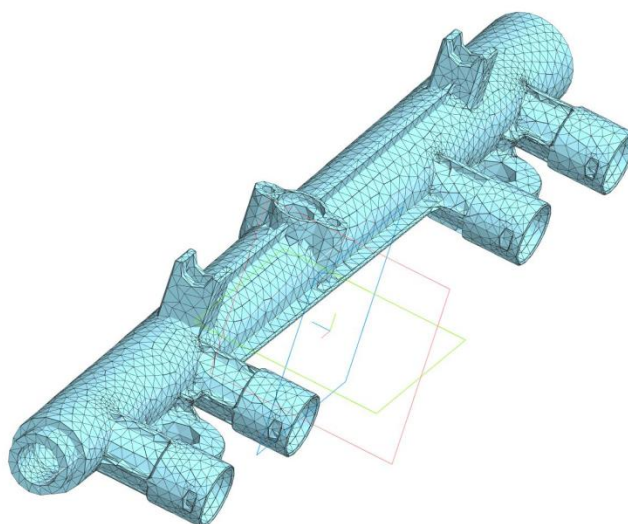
Корпус топливной рампы с сеткой КЭ (вид спереди)
